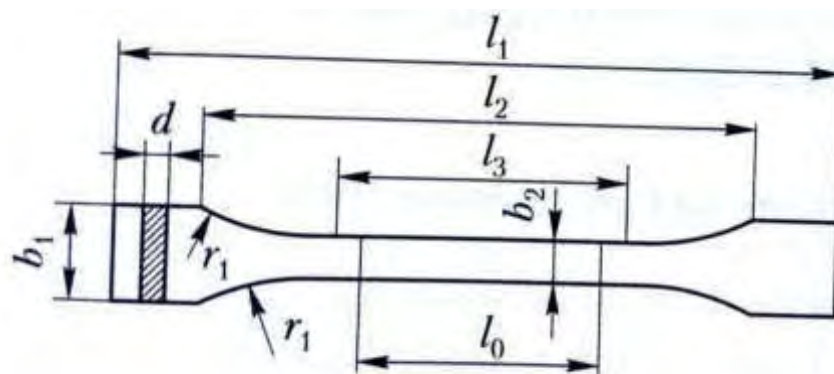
Форма и размеры образцов из ПВХ для испытания на растяжение
